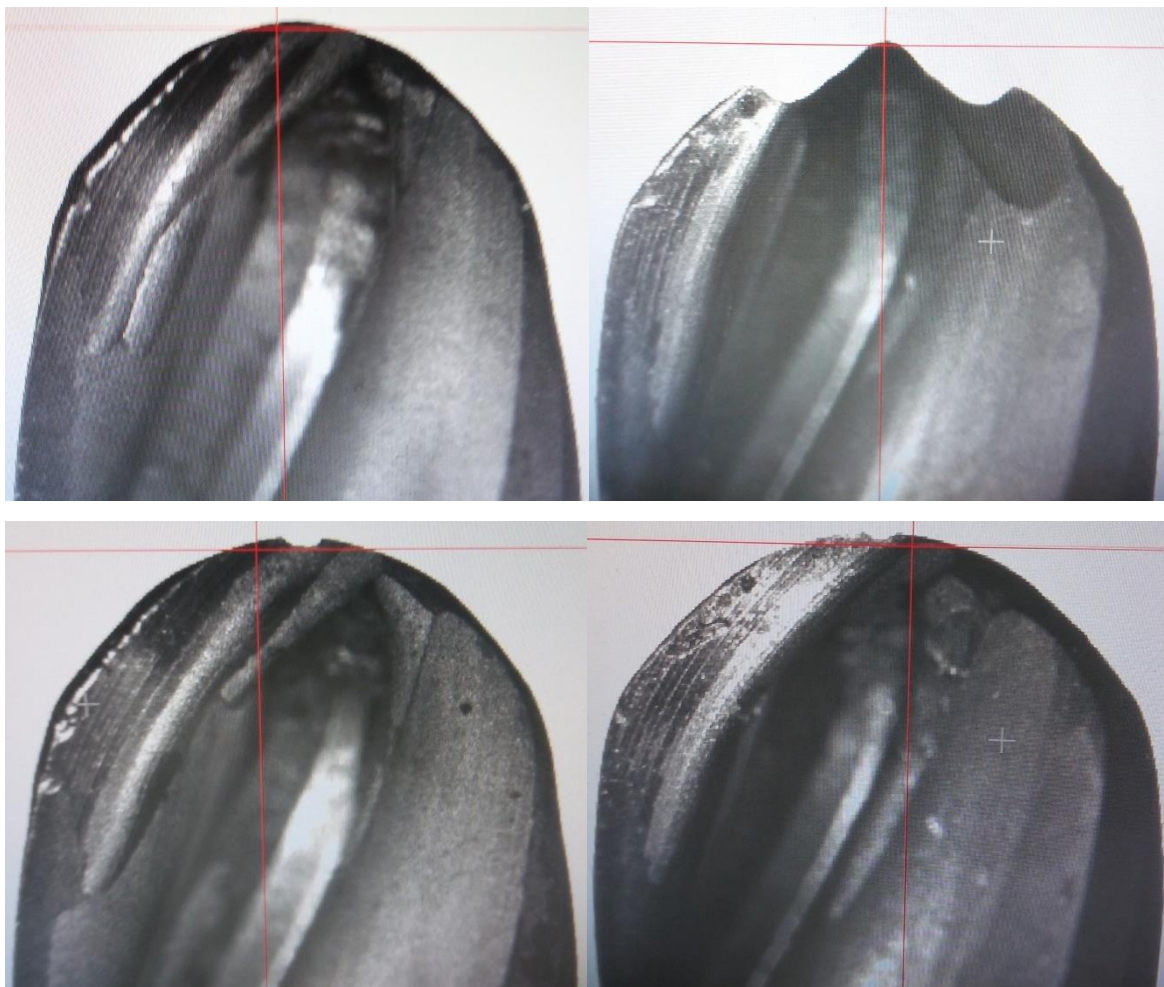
Режущая кромка концевой фрезы без покрытия после обработки 1 лопатки
